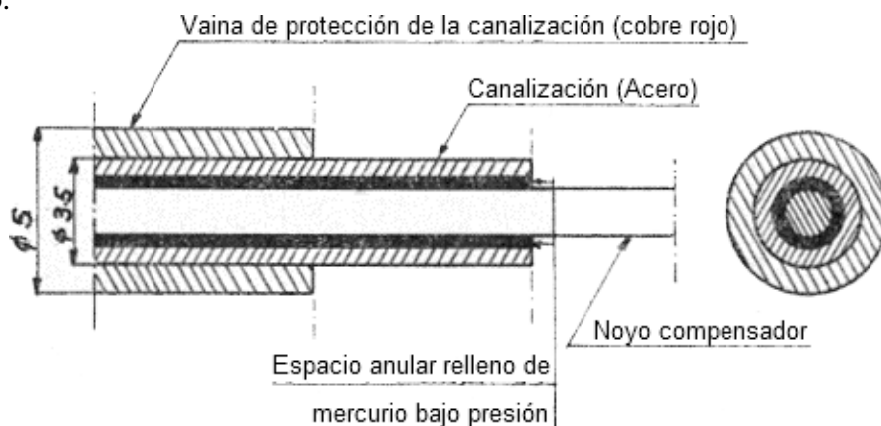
b) Corte de la canalización que va de la caña pirométrica al cuadrante indicador del aparato.
